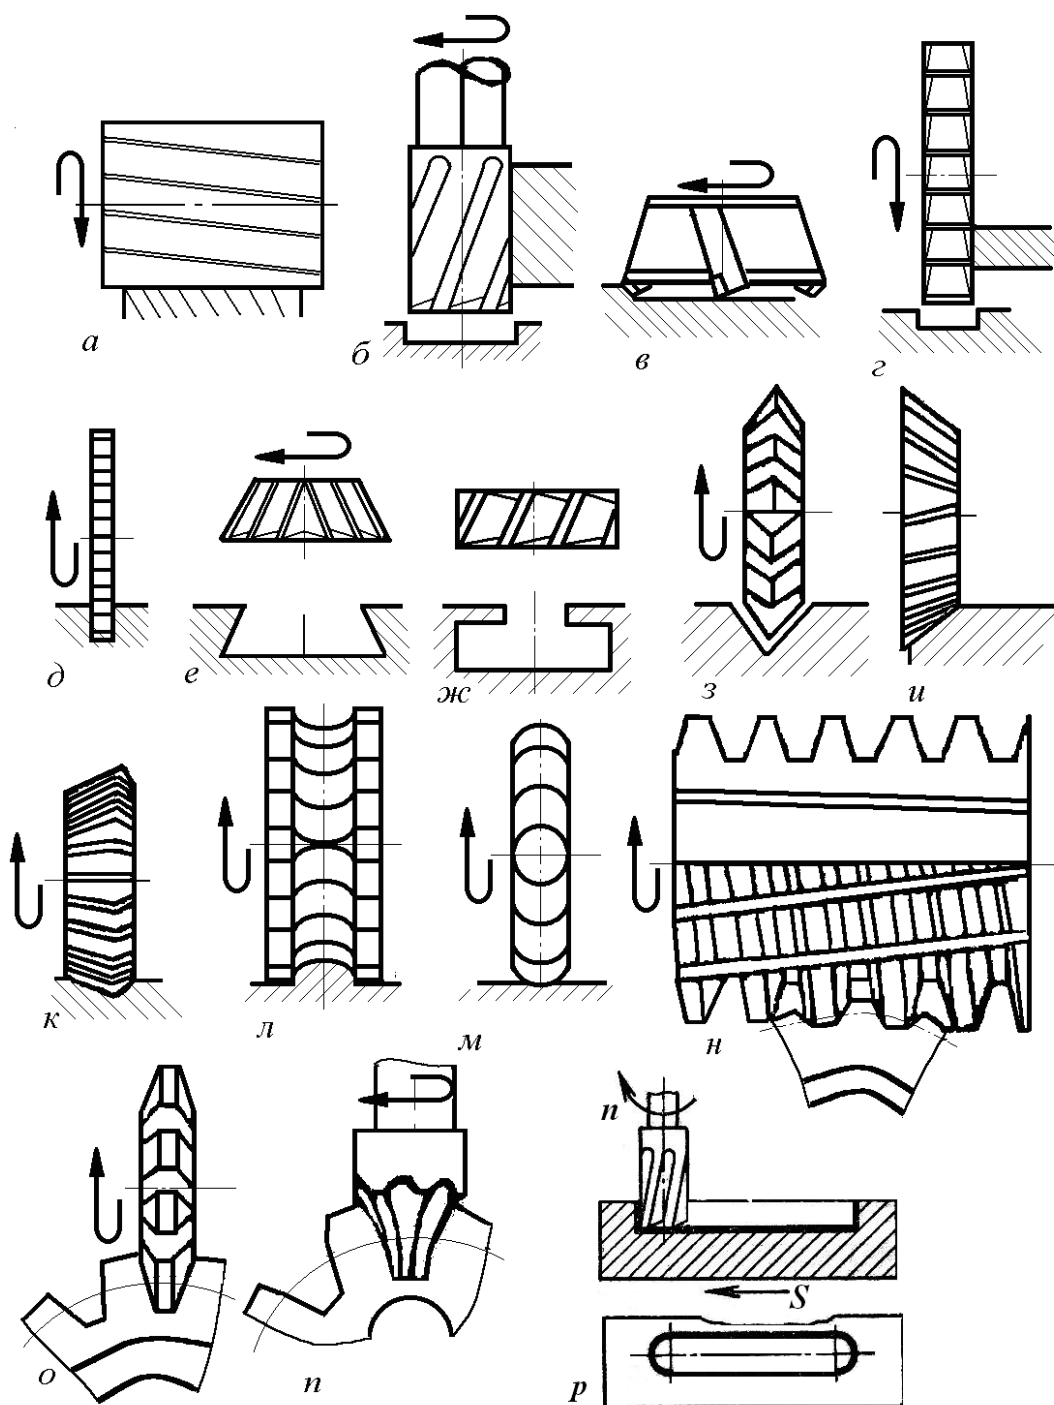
Схемы фрезерной обработки и типы фрез
